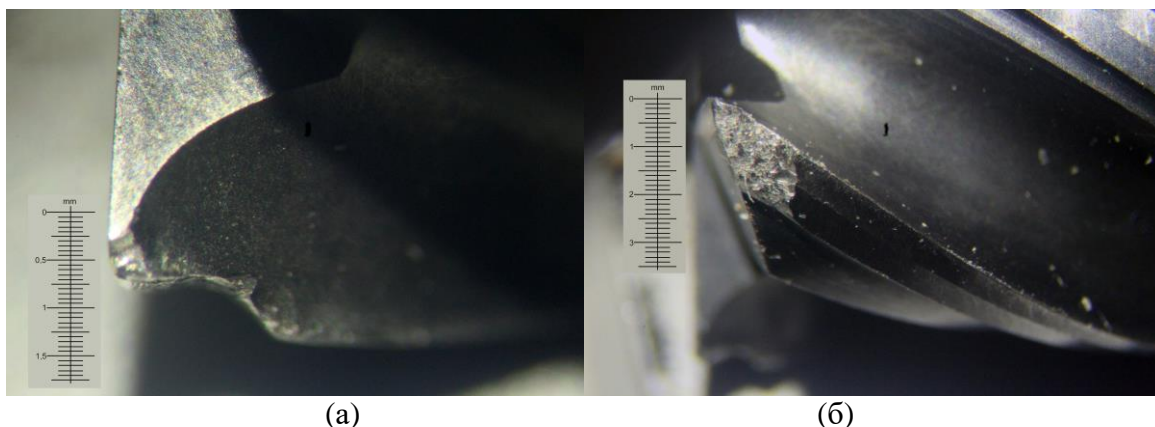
Фотография концевой фрезы. а – фотография передней поверхности зуба фрезы; б - фотография задней поверхности зуба фрезы.
